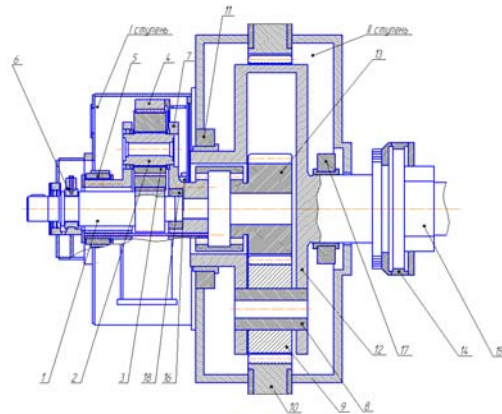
Планетарный редуктор предлагаемой конструкции (2 вариант): 1 - вал-шестерня I ступени; 2,8 - ось сателлита; 3,9 - сателлит; 4,10 - зубчатый венец; 5,11,16,17 - подшипники скольжения водила; 6 - подшипники скольжения вала-шестерни I ступени; 7,12 - водило; 13 - солнечная шестерня II ступени; 14 - зубчатая муфта; 15 - провал; 18 - подшипник скольжения (втулка вала-шестерни)
